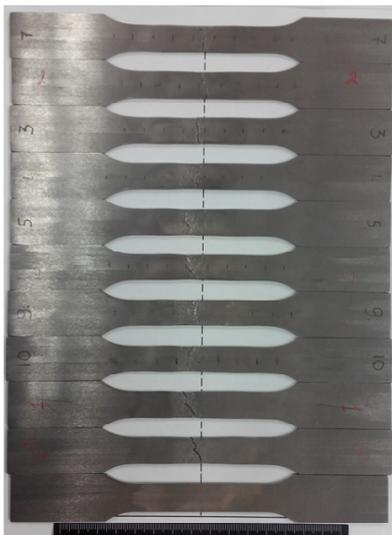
Внешний вид сварных образцов после разрушения
